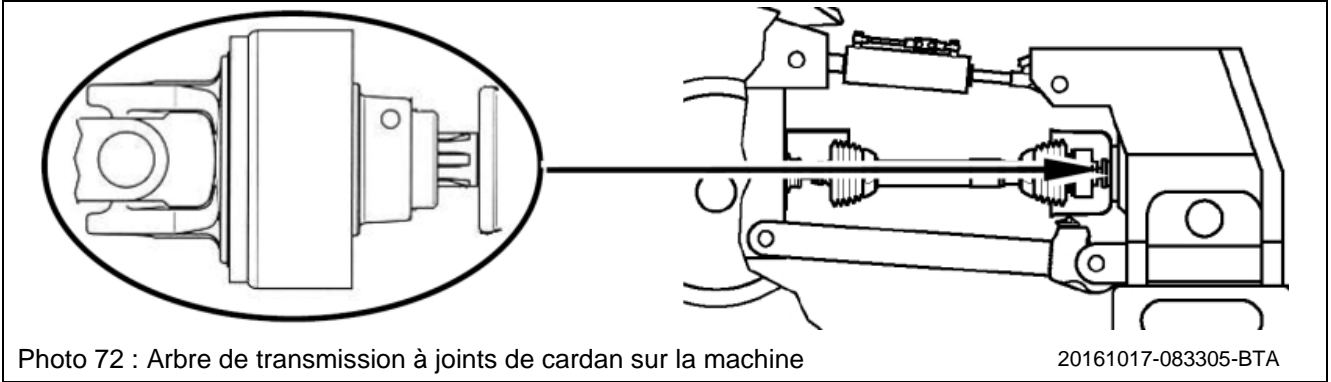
Arbre de transmission à joints de cardan sur la machine
